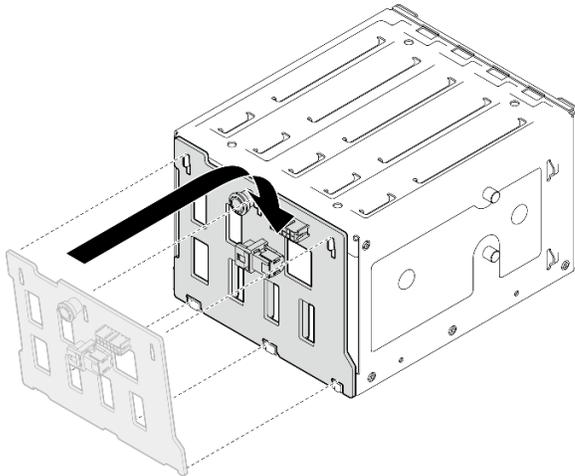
Installation du fond de panier d’unité remplaçable à chaud
